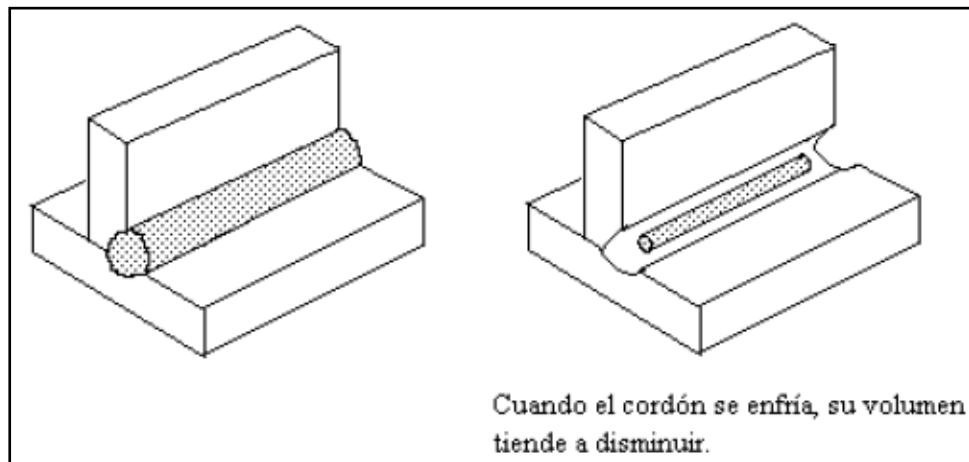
Enfriamiento del cordón de soldadura. (The Procedure Handbook of Arc Welding, 1995.)
